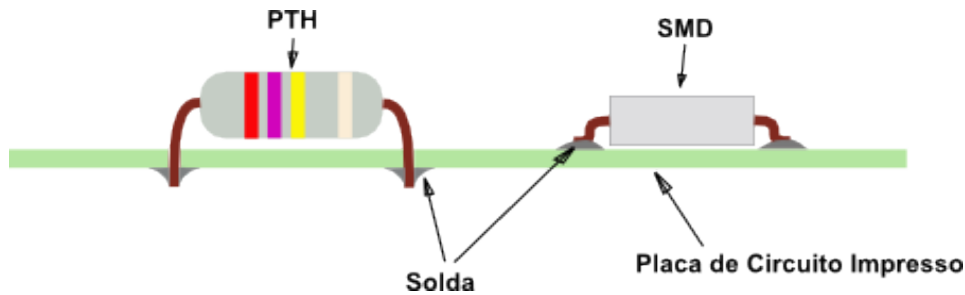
Soldaduras de componentes *through hole* y montaje superficial
